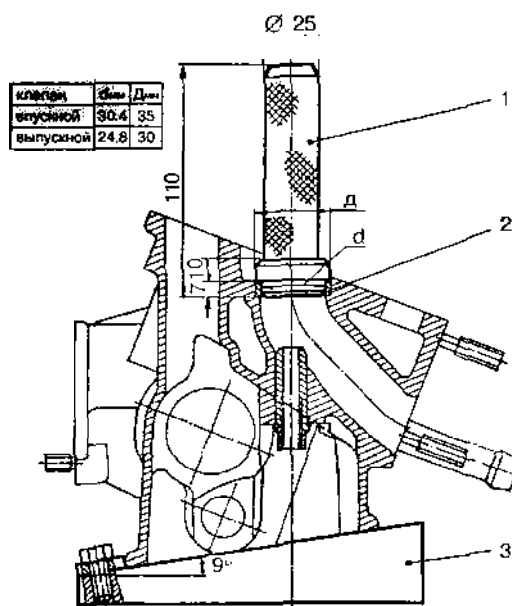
Оправки для запрессовки седел клапанов: 1 - оправка; 2 - седло клапана; 3 - подставка.
